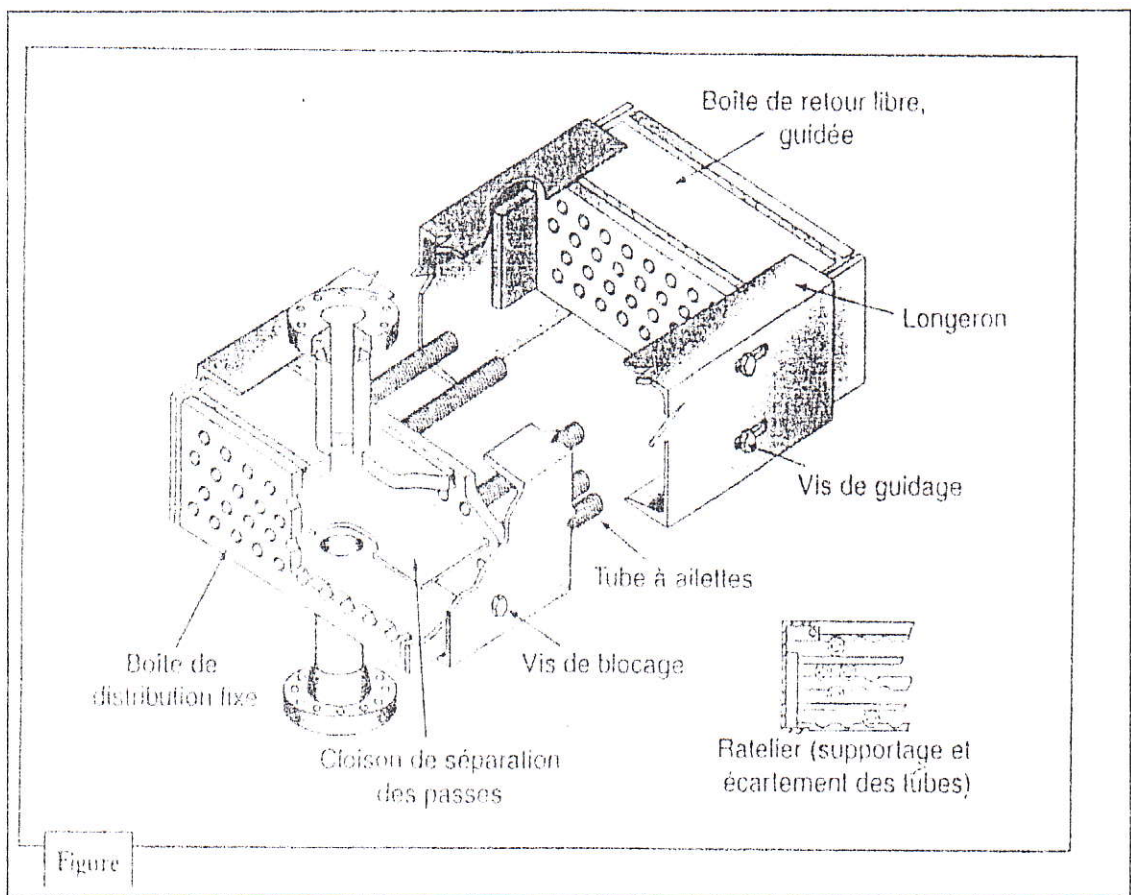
Assemblage d'un faisceau à collecteur à bouchons
